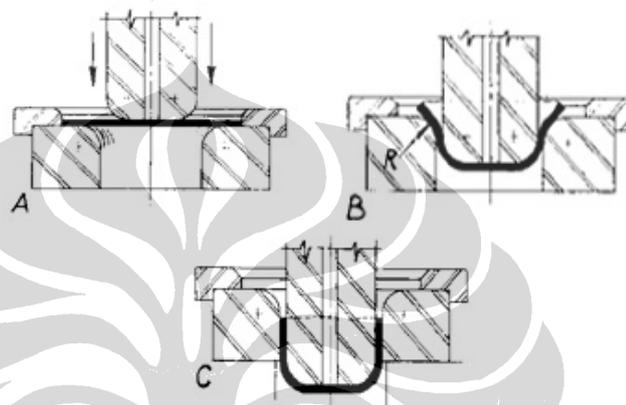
16 Blank dan Beberapa Macam Bentuk Draw Piece
